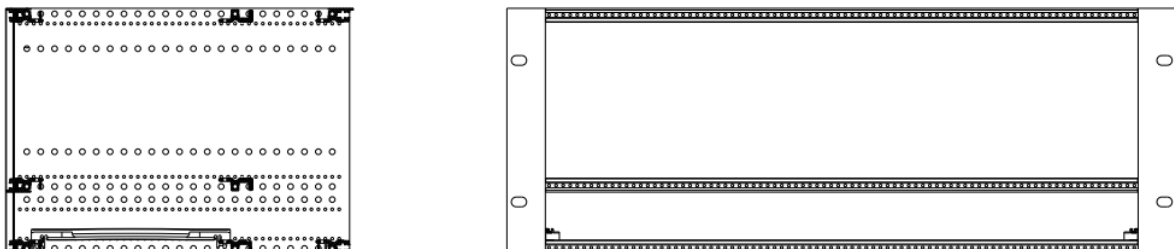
Seiten- und Frontansicht Baugruppenträger
